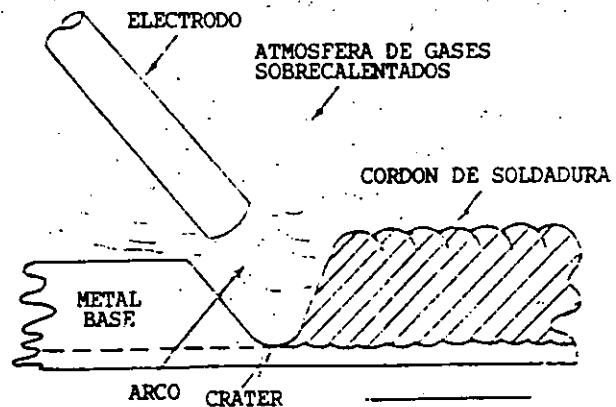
FIG. _____ SOLDADURA DE ARCO DE UN ELECTRODO DESNUDO EN PROCESO
